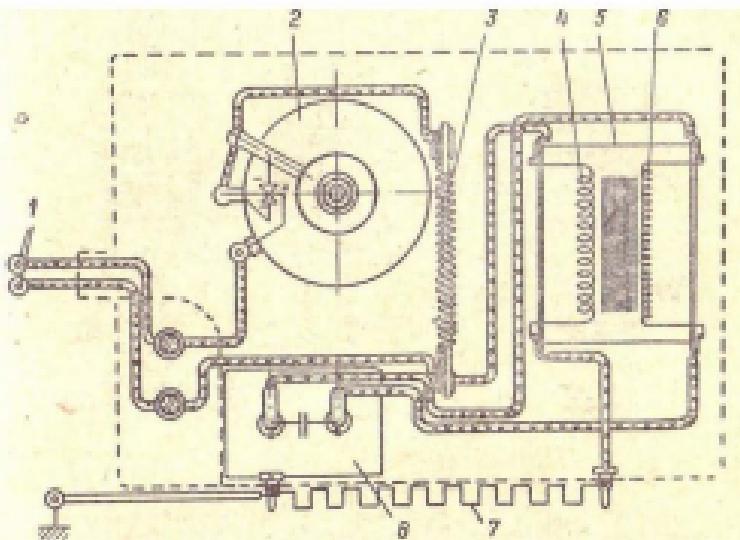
Стабилизатор напряжения мотороллера „Ватка”:
